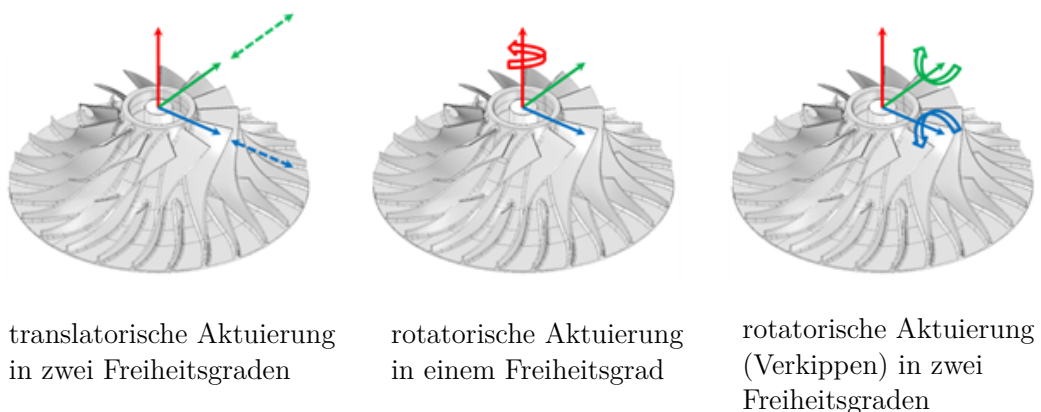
Möglichkeiten zur Aktuierung des Impellers [216].
